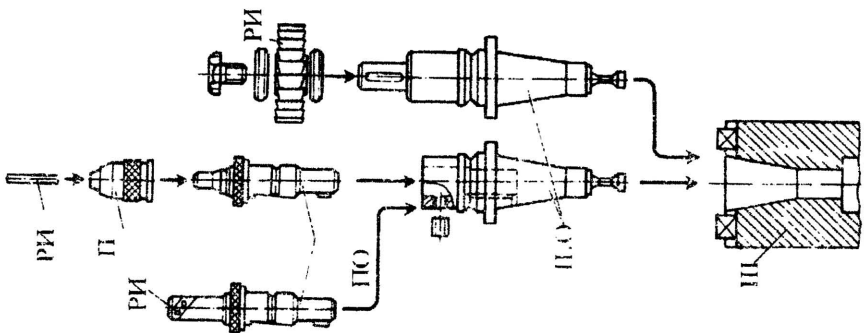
Схема построения комплекта инструмента: ШО – оправка, закрепляемая в шпинделе станка; Ш – шпиндель, ПО – переходная оправка, П – патрон, РИ – режущий инструмент
